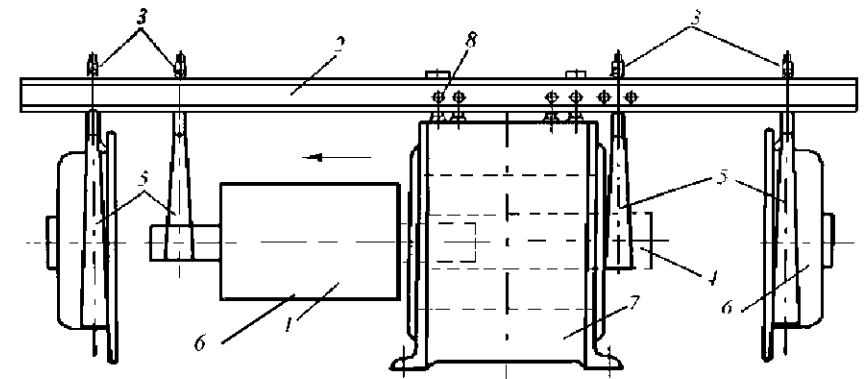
Приспособление для разборки и сборки электрических машин без грузоподъемного механизма:
